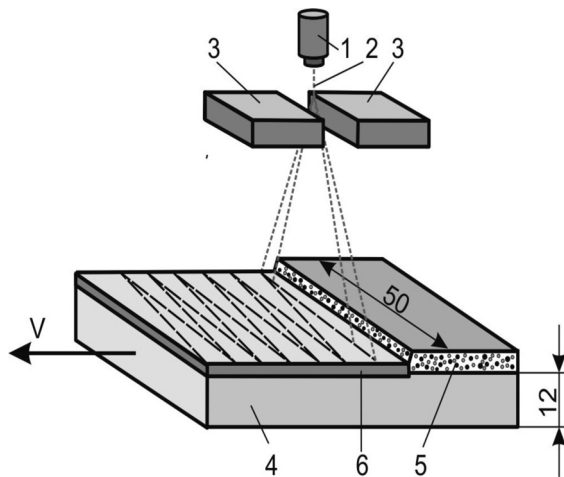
Схема электронно-лучевой наплавки алюминиево-титановой смеси на заготовки из сплава ВТ1-0:
